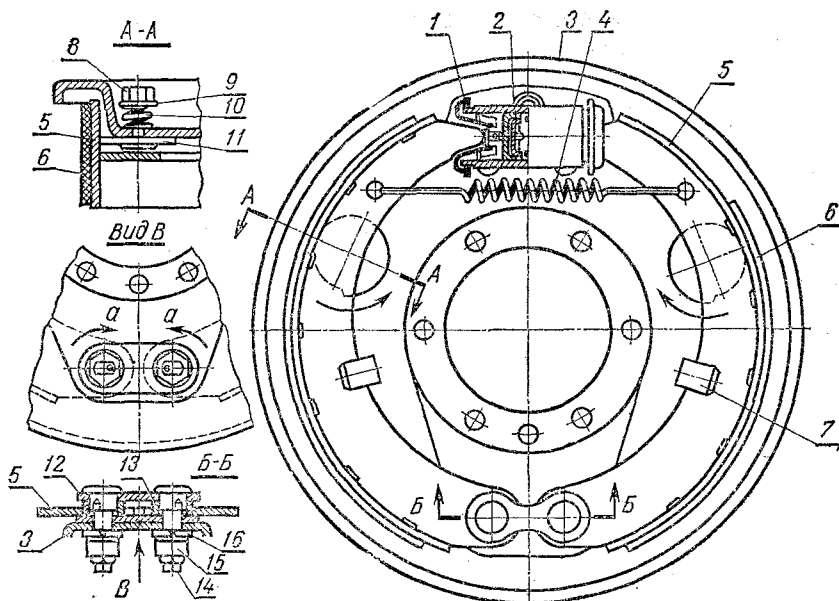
Колесный тормоз автомобиля ГАЗ-53А:
